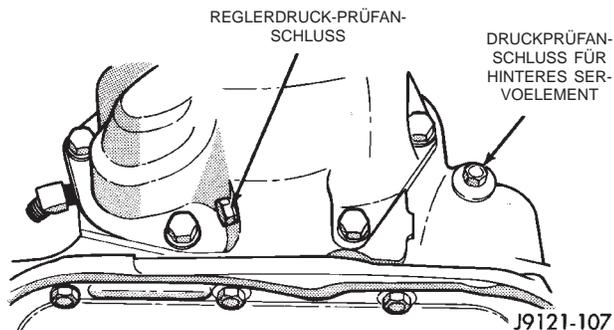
Druckprüfanschlüsse auf der Gehäuse-Rückseite—Zweiradantrieb
